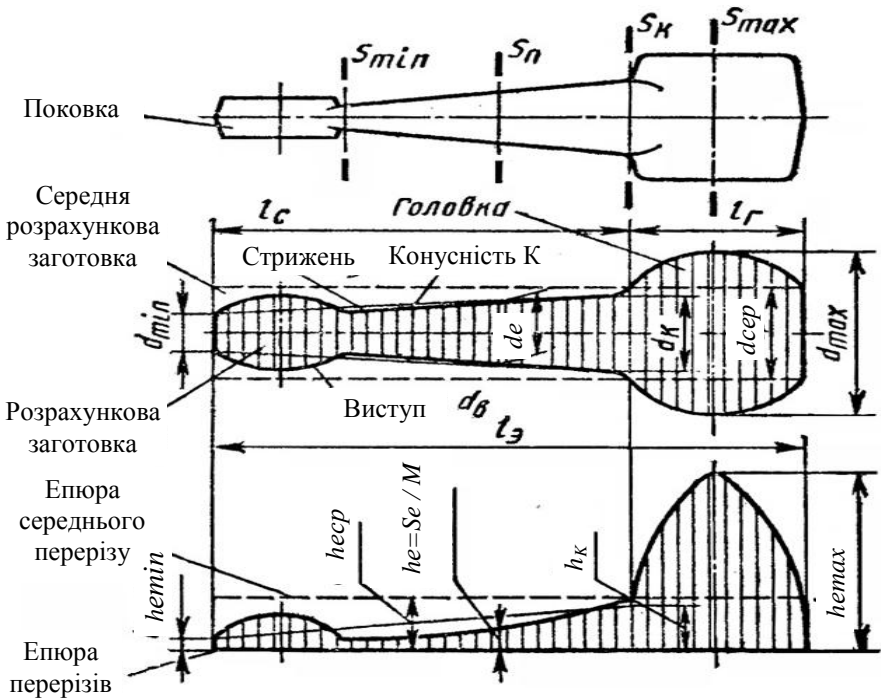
Елементарна розрахункова заготовка та епюра перерізів
